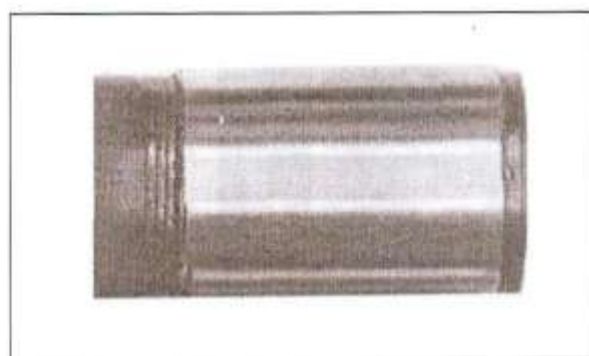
Вид чугунного образца после лазерной наплавки на предварительно оплавленную и отожженную поверхность
